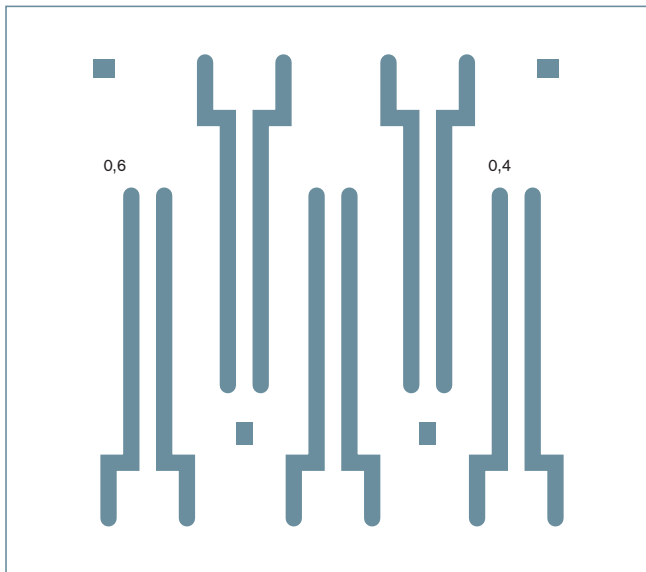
Probeta PCB 50,8 x 50,8 mm.
